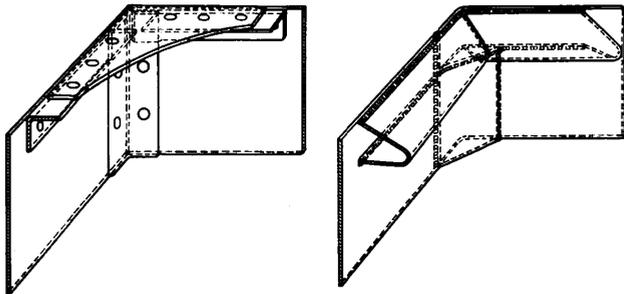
Obere Eckverbindung des Kastenaufbaus in genieteter und geschweißter Ausführung.
